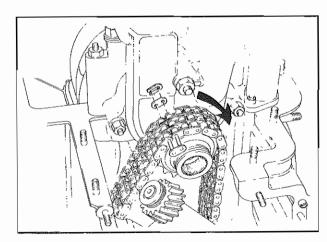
Montaggio molletta di fermo Retaining spring assembly
